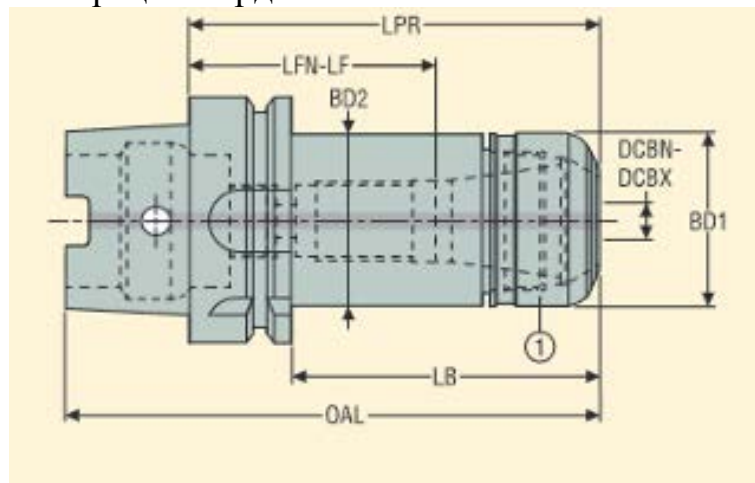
Цанговий патрон для свердла E930456721660 [7, с.102]
